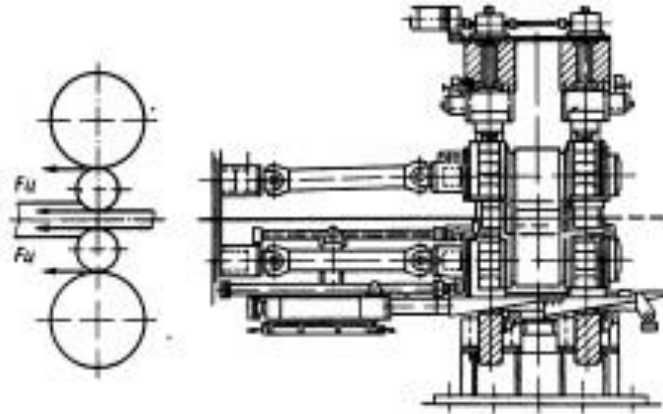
Чотирьохвалковий стан з приводними опорними валками
